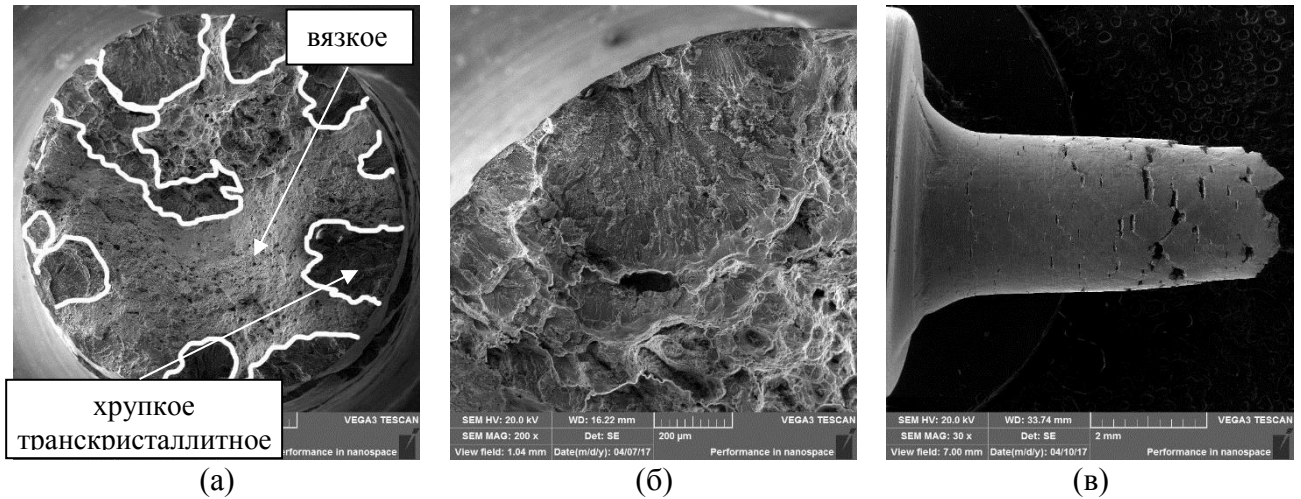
Поверхность разрушения и боковая поверхность образца из стали 08X18H10T в исходном состоянии, испытанного в насыщенной кислородом среде (а – общий вид излома; б – хрупкая транскристаллитная трещина, инициированная от боковой поверхности образца; в – боковая поверхность)
